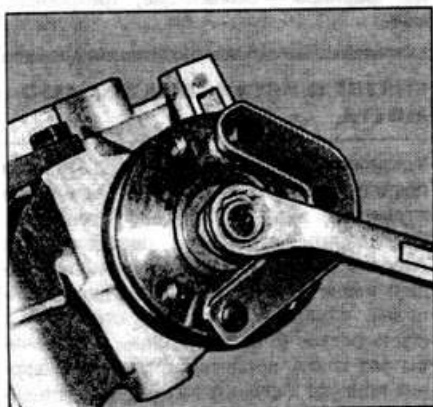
Блокировка фланца ведущей шестерни главной передачи фиксатором 15.040
